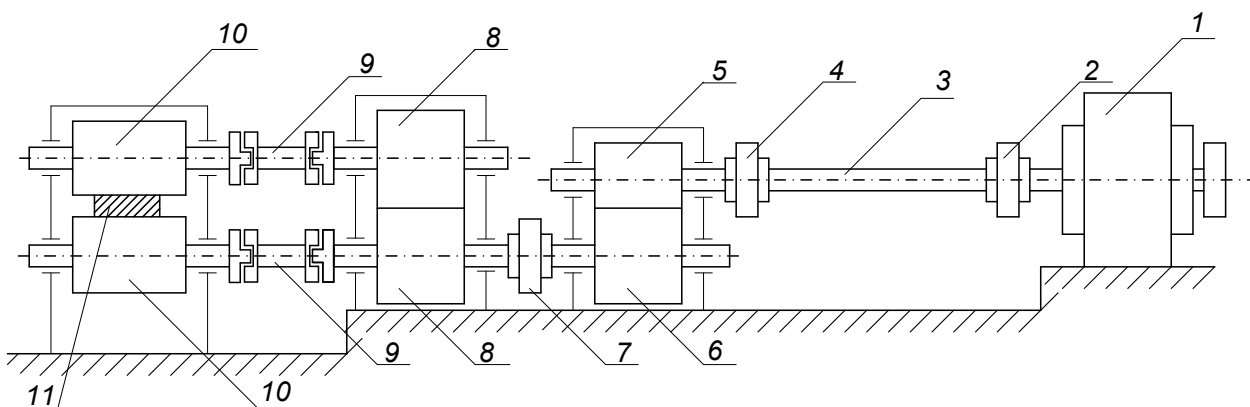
Прокатная клеть с групповым приводом: 1 – электродвигатель; 2,4,7 – муфты; 3 – вал; 5- быстроходная шестерня редуктора; 6 – тихоходная шестерня редуктора; 8 – шестерни шестеренной клетки; 9 – шпиндели; 10 – прокатные валки; 11- слиток
